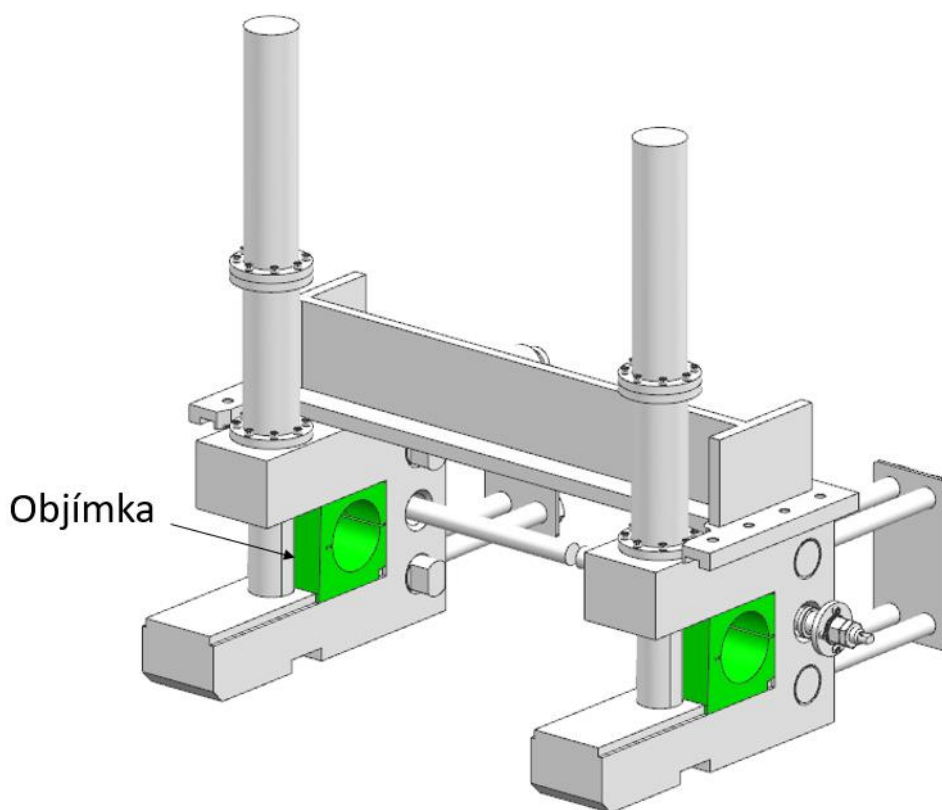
Upevnění testovaných hydromotorů – přední pohled
